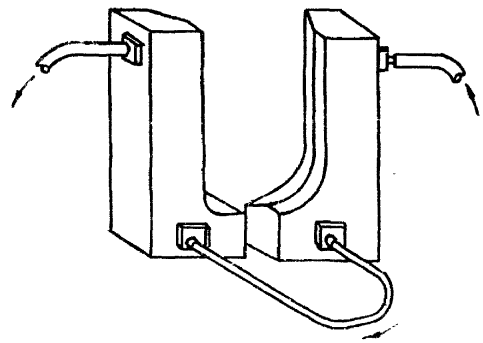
Общий вид охлаждаемых водой форм для ванны одноэлектродной сварки
